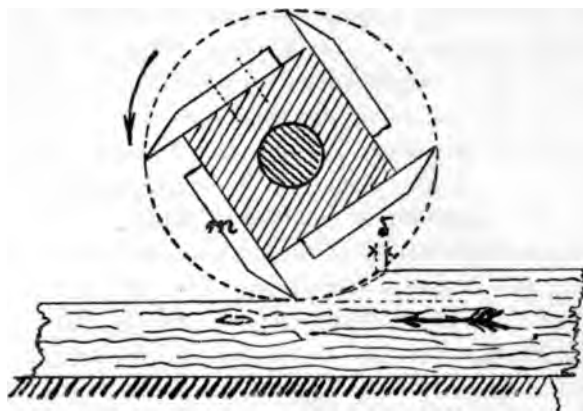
Zeigt die Zuführungsrichtung bei Holzhobelmaschinen.
